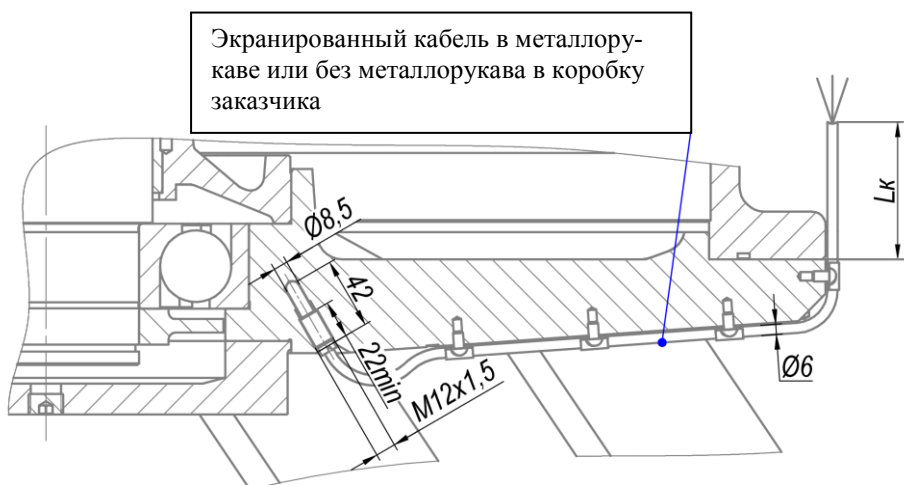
Вариант установки датчиков контроля температуры подшипников без коробки выводов двигателей ВАБ450
